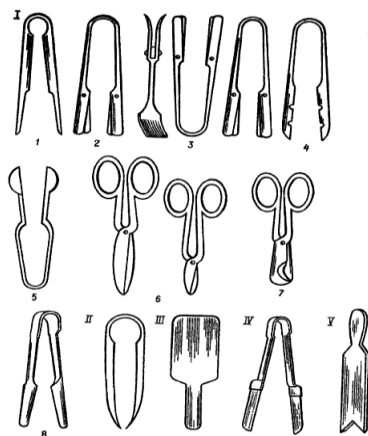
Допоміжні інструменти для ручного видування:
